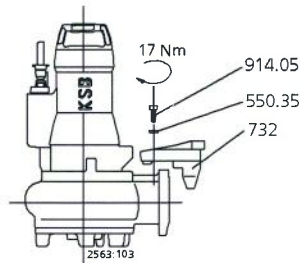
Montage de la griffe pour guidage par câble, par 1 barre et par étrier
